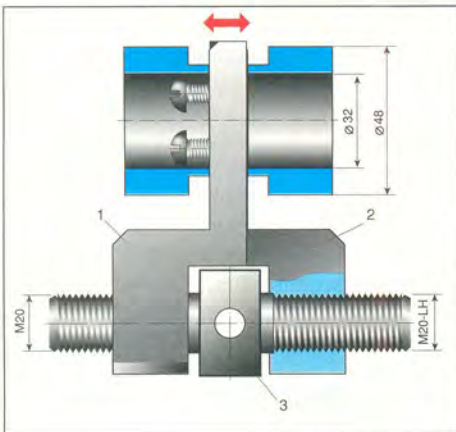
Приспособление для “разрабатывания” поршней в тормозных цилиндрах: 1, 2 – лапки; 3 – винт.
